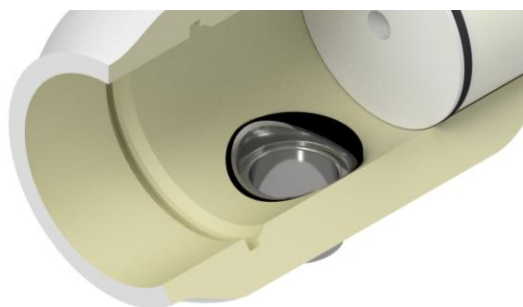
Después del primer corte habremos eliminado la mitad del exceso de goma.
